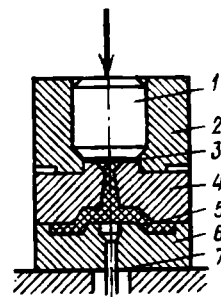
Схема литьевого прессования термореактивной пластмассы:
